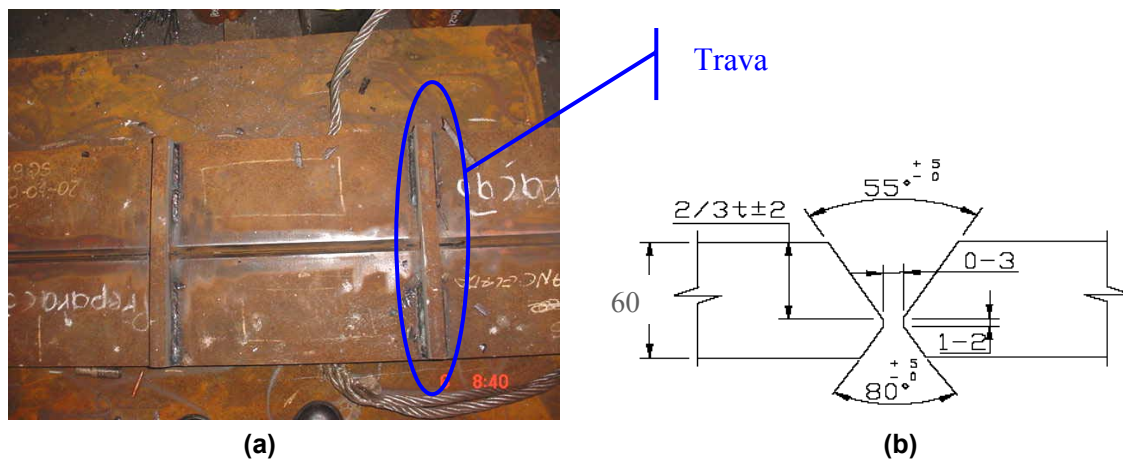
Junta de teste. (a) Junta montada; (b) Croqui do chanfro da junta (dimensões em milímetro).
